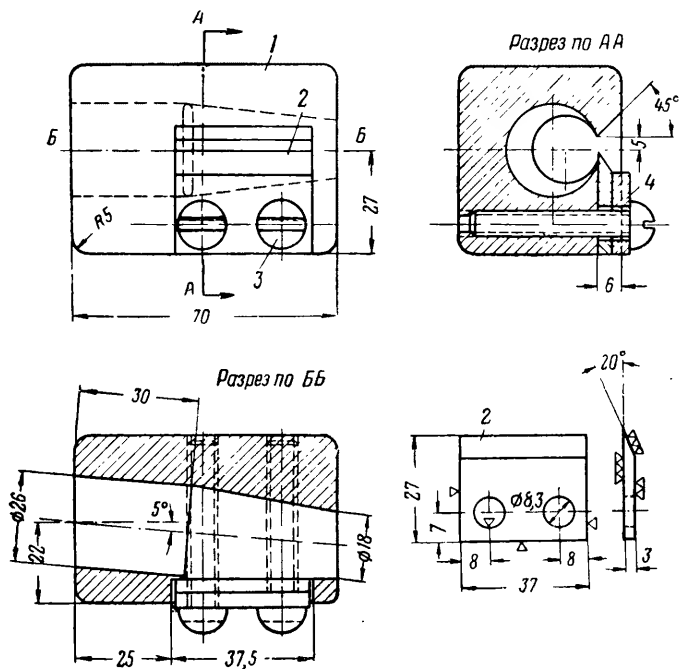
Фрезы для разделки концов миканитовых трубок:
